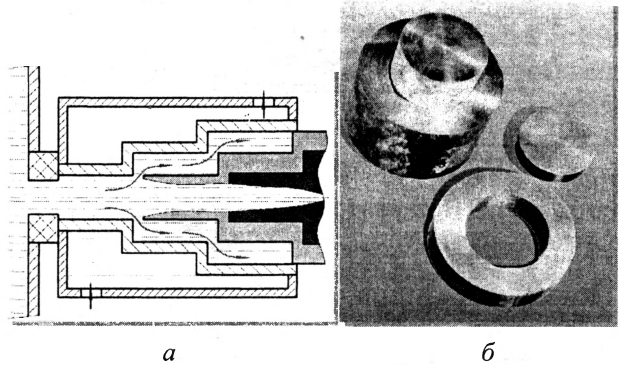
Формирование телескопического слитка: а — схема формирования; б — сплошная и полая заготовки
